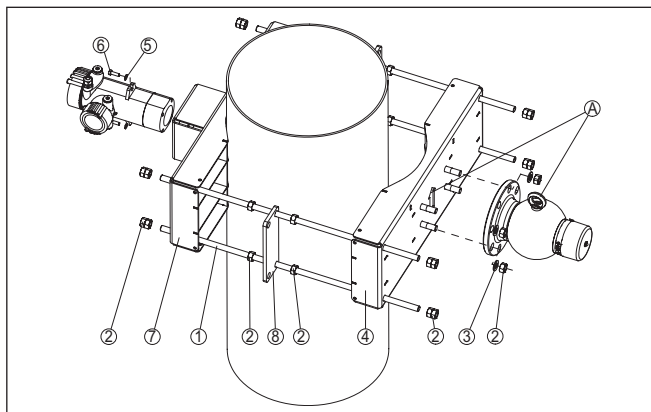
Dispositivo de fixação KV 31 com sensor montado na posição horizontal
